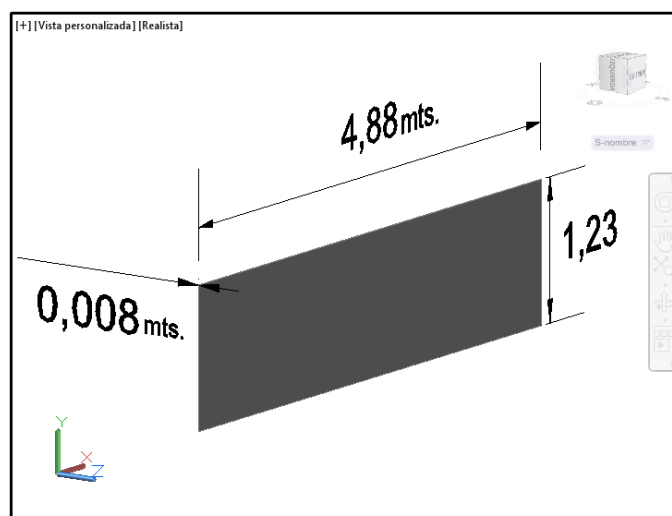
12 – Medidas para la plancha de la estructura del fondo.
